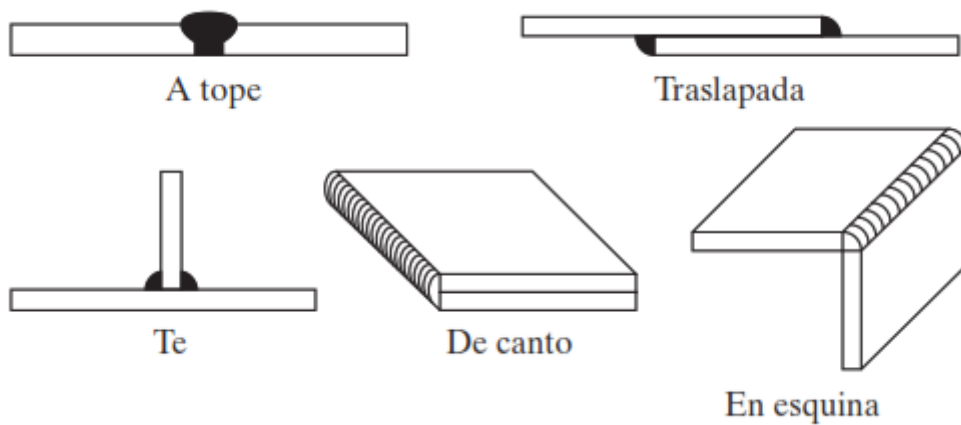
Tipo de juntas soldadas (McCormac & Csernak, 2012)
